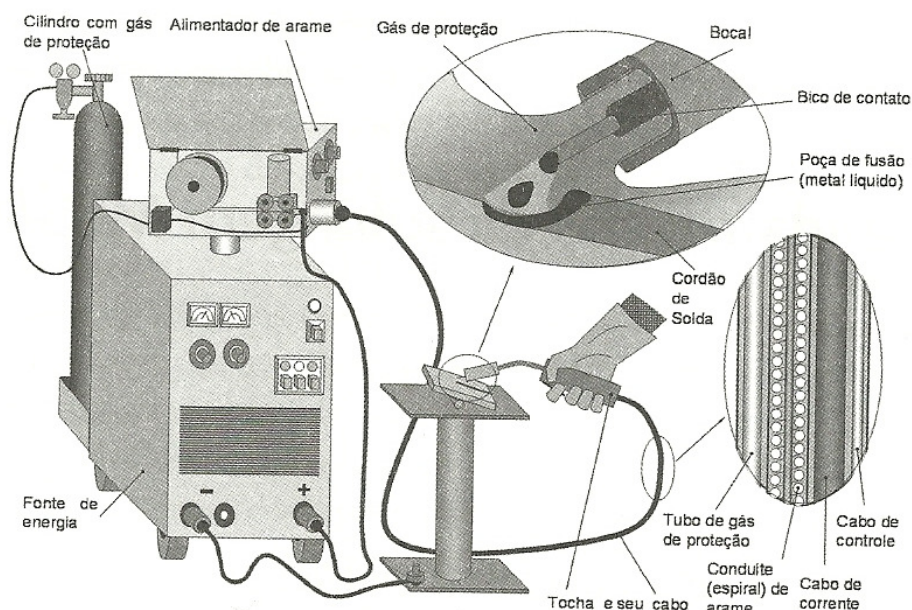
Equipamento de Soldagem GMAW (SCOTTI e PONOMAREV, 2008)
